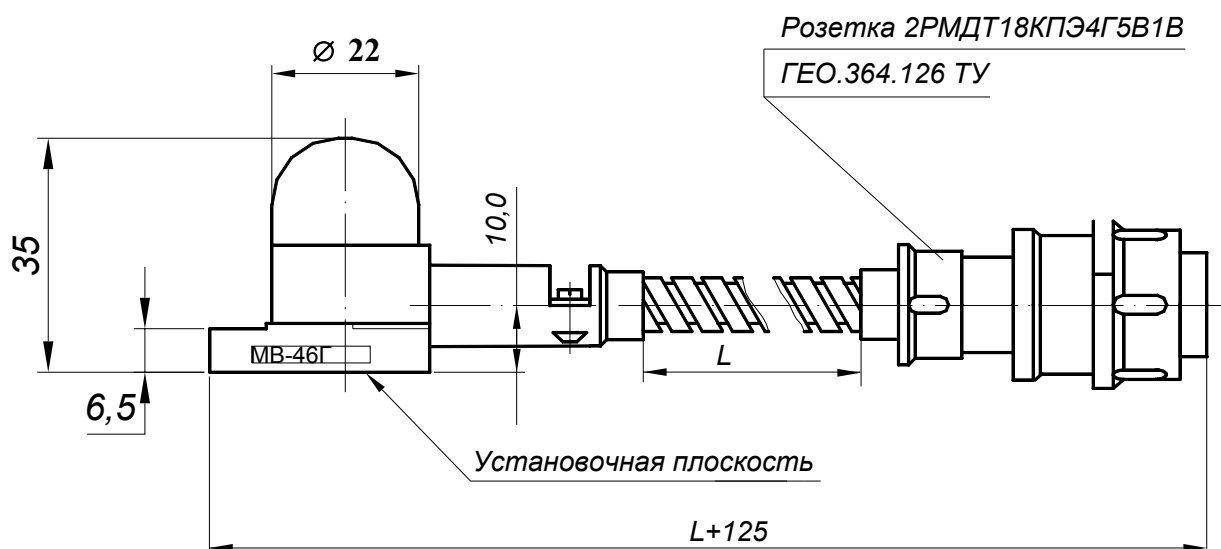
Габаритно-установочные размеры вибропреобразователя МВ-46Г1/L
